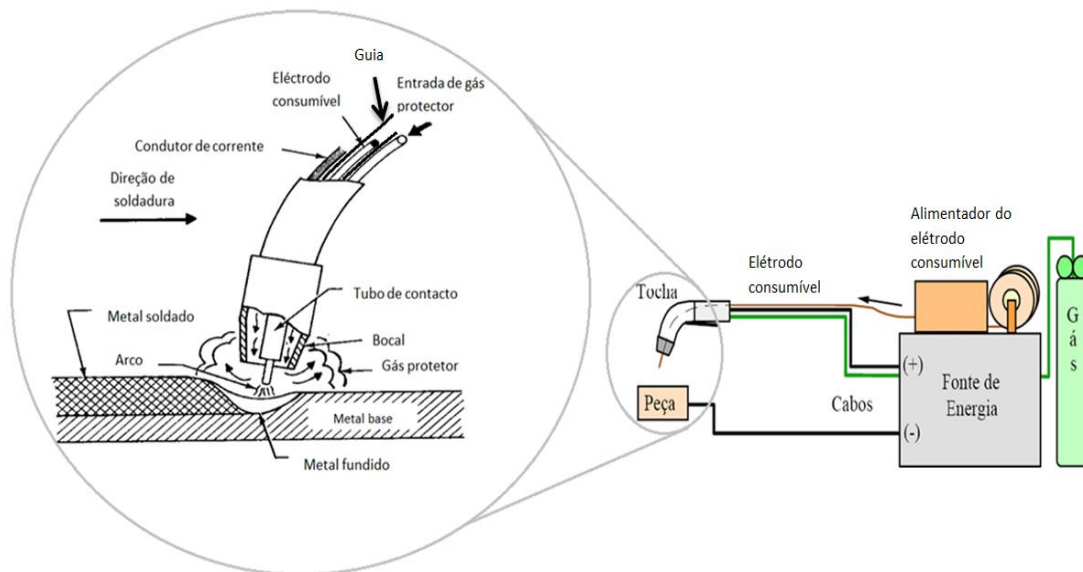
Esquema de equipamento para soldadura MIG.^[15]
